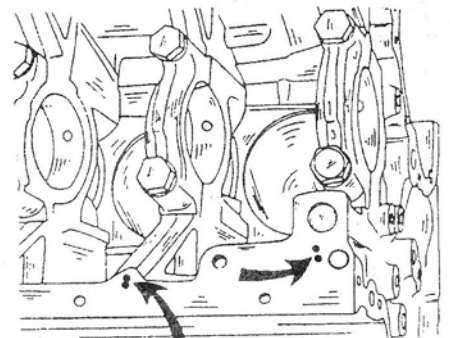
Стрелки указывают на кернения для маркировки допусков отверстия коренного подшипника. Вкладыши подшипников устанавливать в соответствии с маркировочным кернением.
